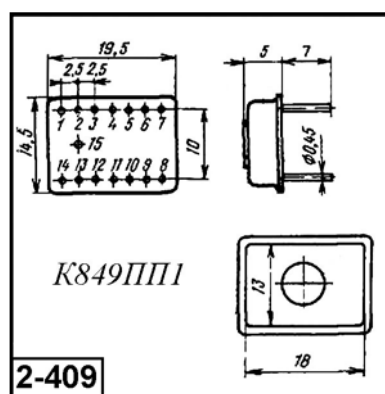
Внешний вид и габаритные размеры преобразователя К849ПП1
